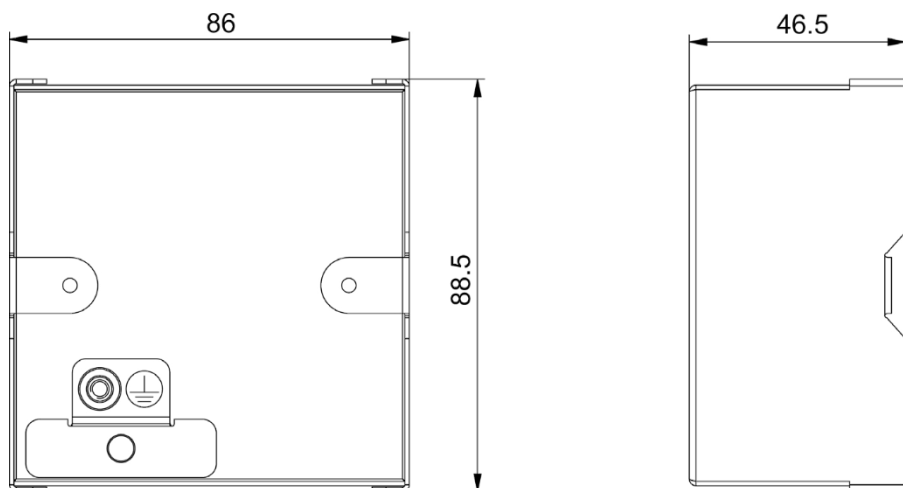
Dimensioni della scatola di cablaggio installata a parete
